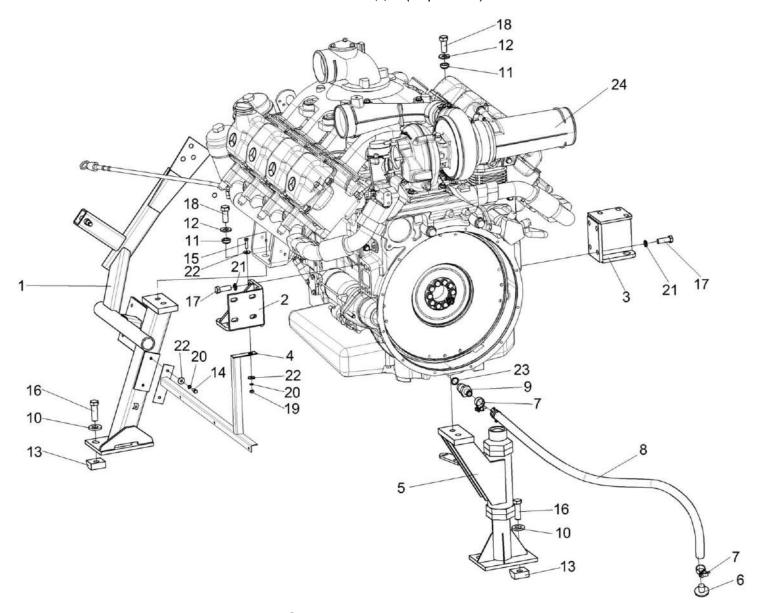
Установка двигателя ОМ 502LA КВК 0150000 (установка двигателя на опорах)
